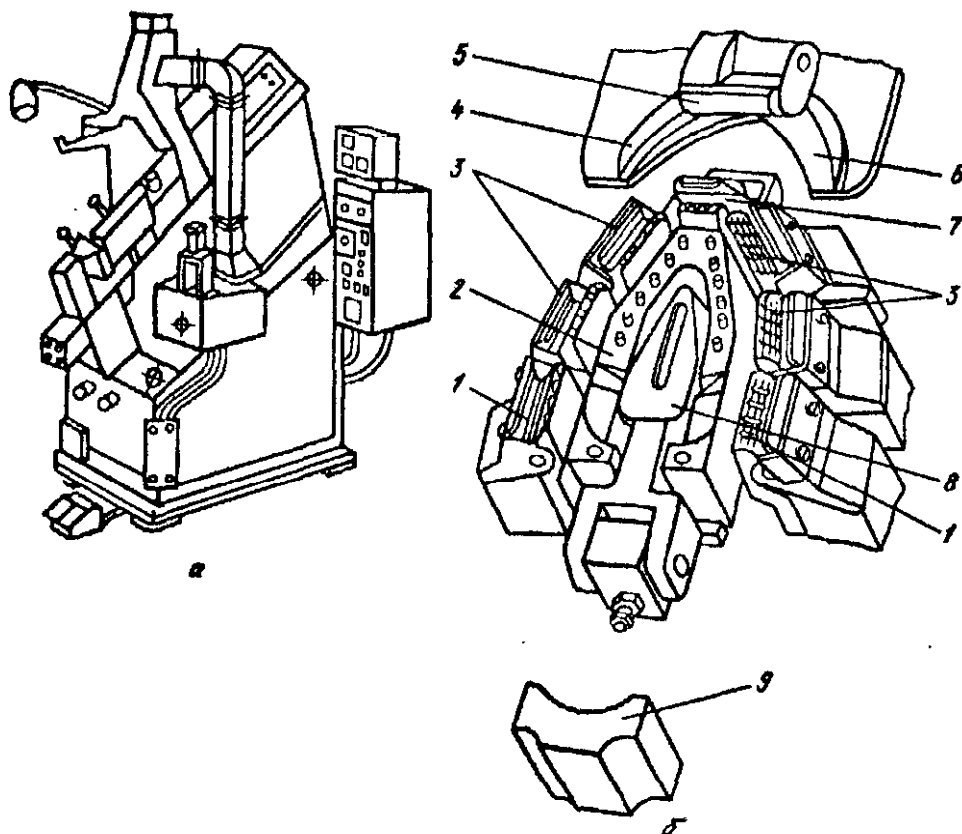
Машина ЗНК-2М-О: а — общий вид; б — рабочие органы
